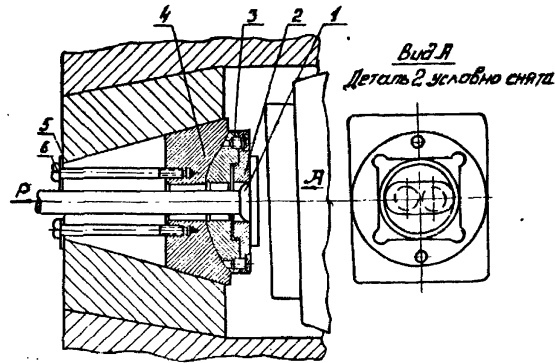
Конструктивная схема приспособления к горизонтальной разрывной машине для испытания на отрыв тавровых соединений.
